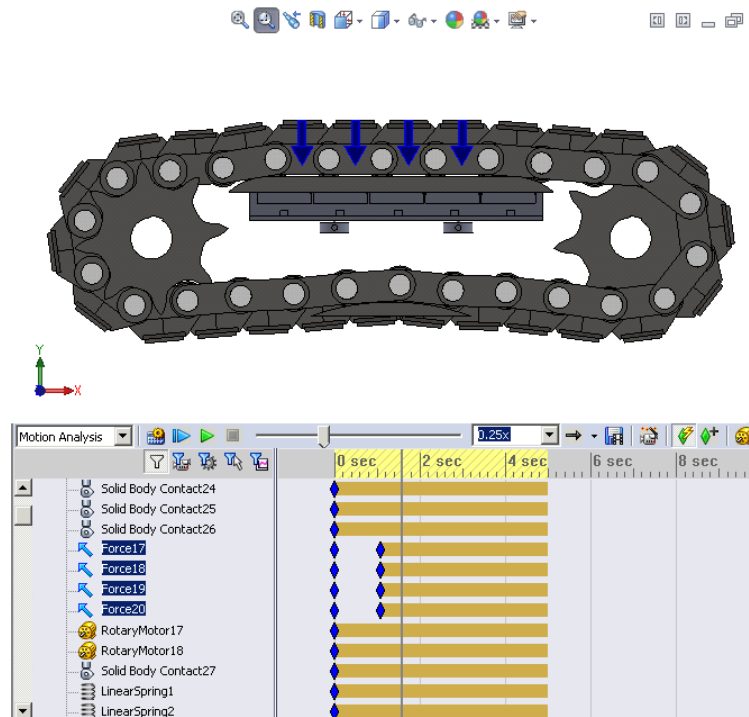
Cargas normales aplicadas sobre los eslabones de apoyo.
